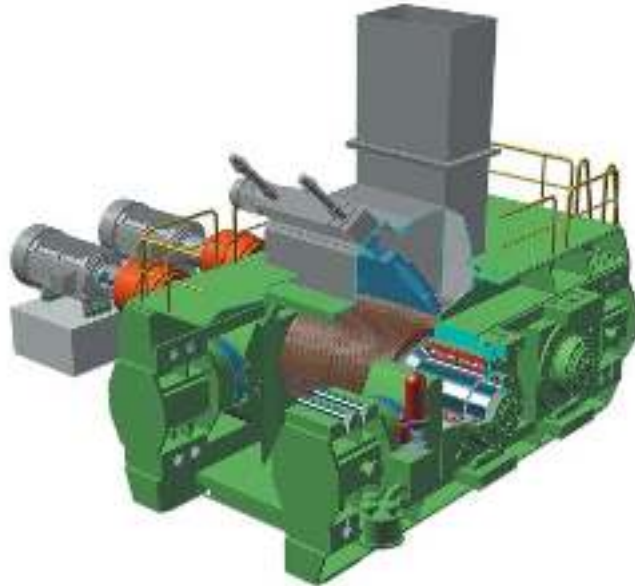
Общий вид прессвалкового измельчителя
